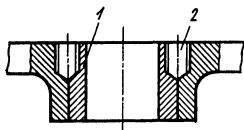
Эскиз отремонтированного подшипникового щита
